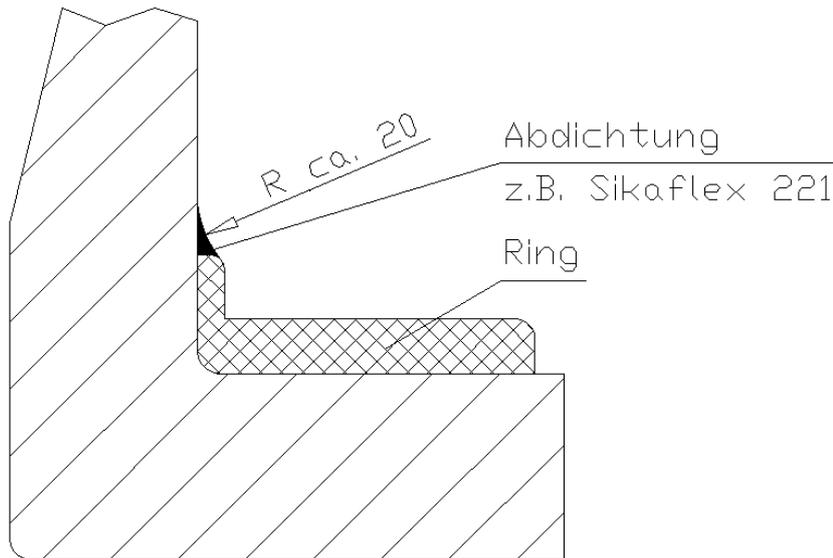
Beispiel für die Abdichtung an einem Stahlflansching
